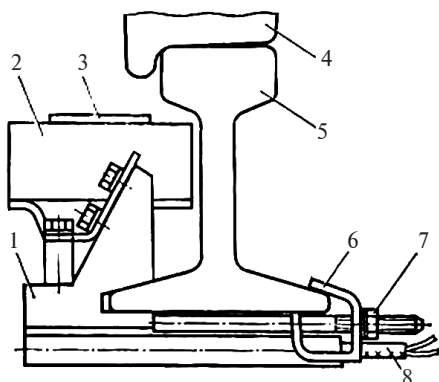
Датчик прохода колёс ПБМ: 1 – кронштейн; 2 – катушка; 3 – постоянный магнит; 4 – гребень колеса; 5 – подошва рельса; 6 – скоба; 7 – гайка; 8 – соединительный кабель.
